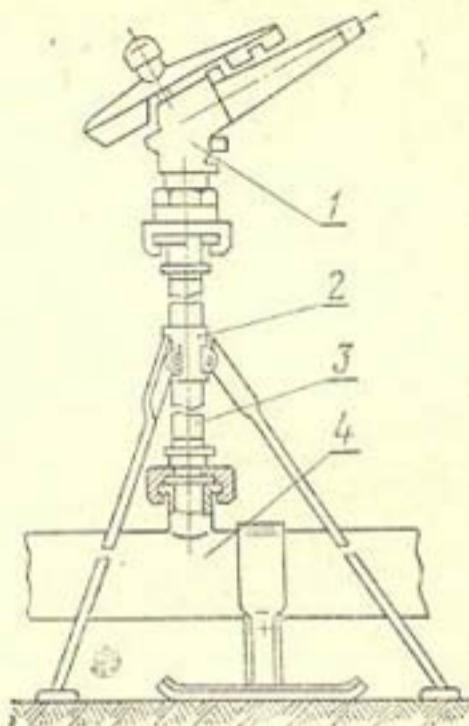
Крепление среднеструйного дождевального аппарата «Роса-3» на удлиненной стойке рабочего трубопровода КИ-50:
